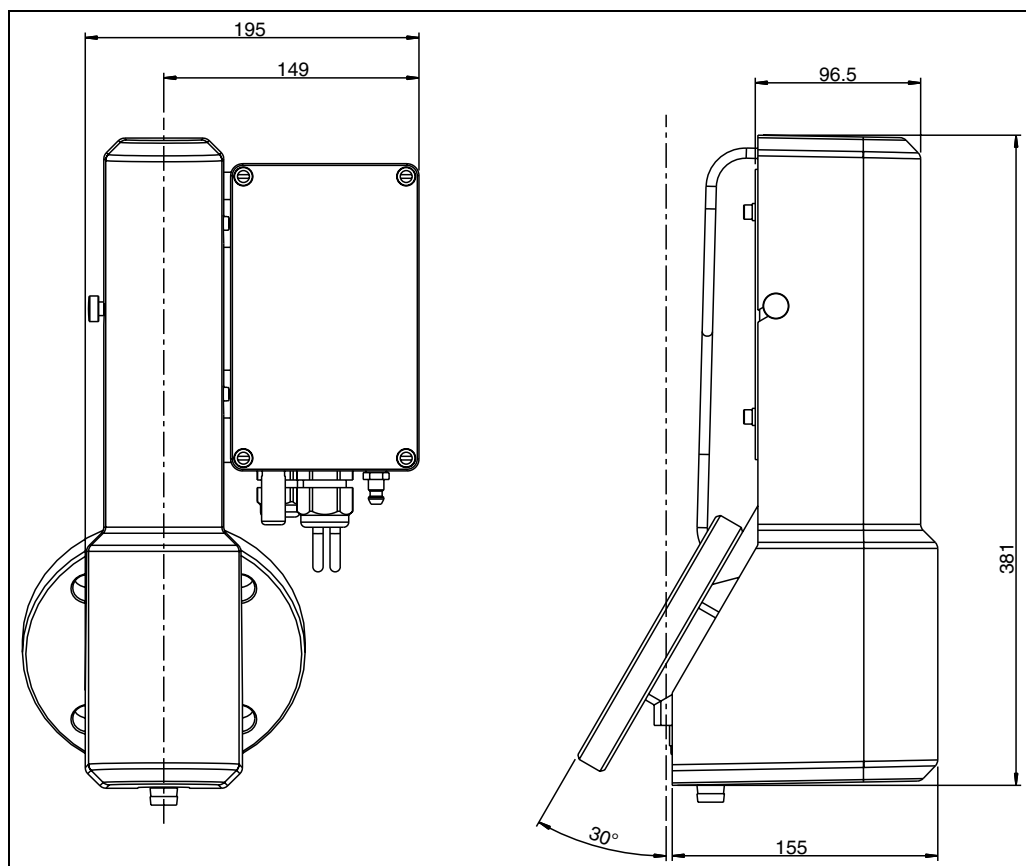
Abmessungen der Sampler Armatur ASP Inline mit 5 ml Probevolumen (Angaben in mm)
